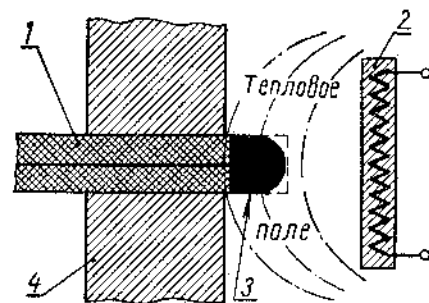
Схема образования торцового шва в тепловом поле ленточного нагревателя:
